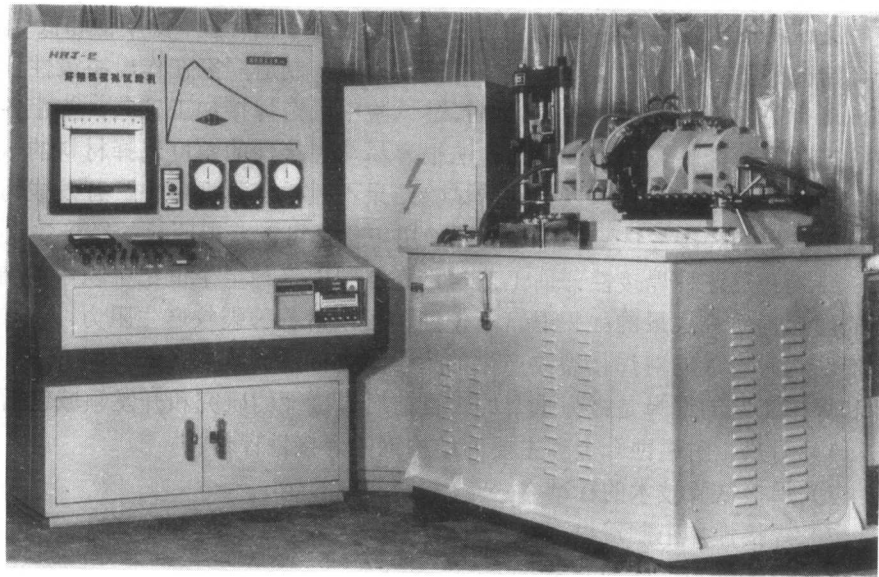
国产 HRJ—2 型焊接热循环模拟试验机
